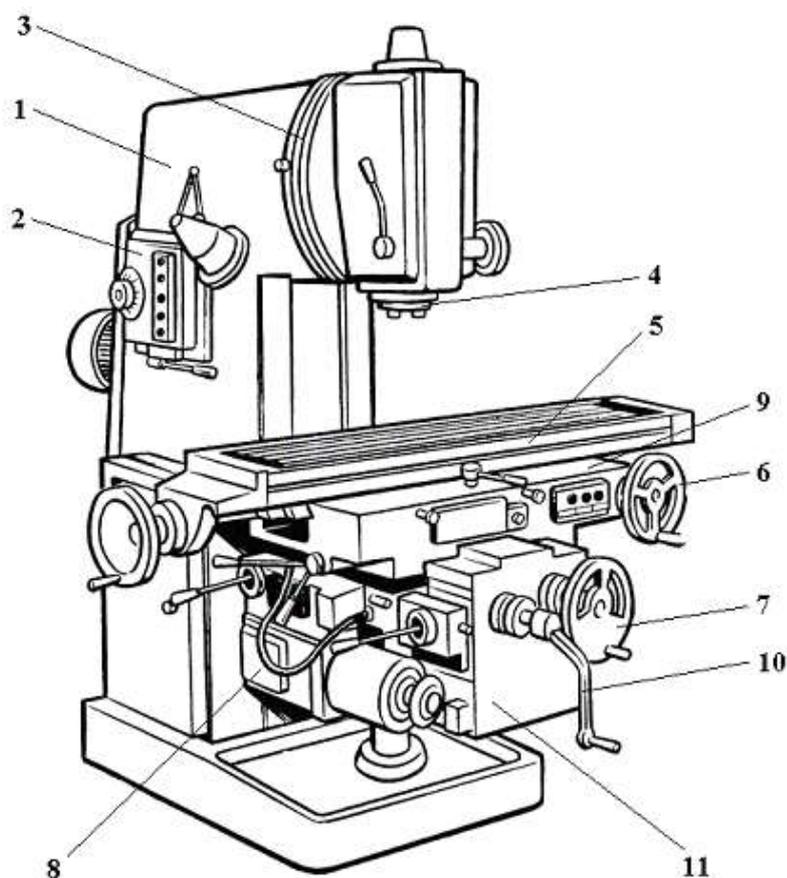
Вертикально-фрезерный станок: 1 – станина; 2 – коробка скоростей; 3 – механизм для поворота шпиндельной головки в вертикальной плоскости; 4 – шпиндель; 5 – рабочий стол; 6 – маховик, служащий для ручного перемещения стола в продольном направлении; 7 – маховик, служащий для ручного перемещения стола в поперечном направлении; 8 – коробка подач; 9 – салазки, по которым осуществляется перемещение стола; 10 – рукоятка для ручного перемещения стола в вертикальном направлении; 11 – консоль
